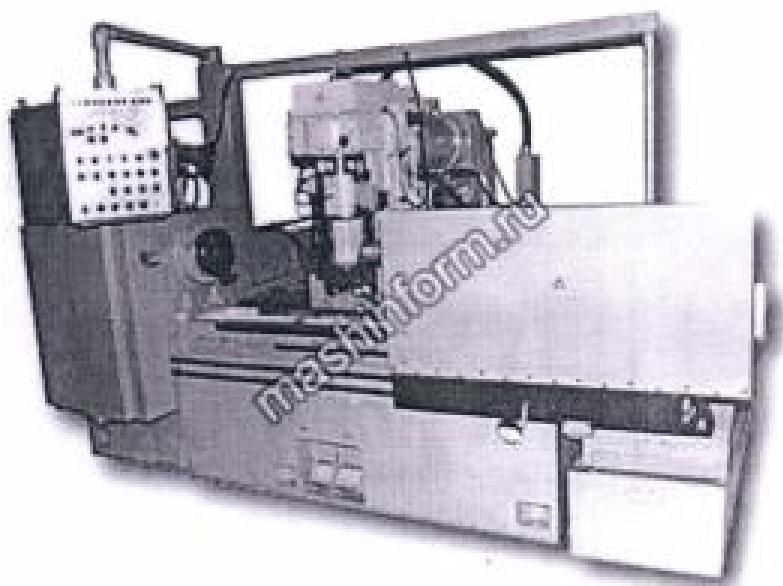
Загальний вигляд токарно-фрезерного верстата
